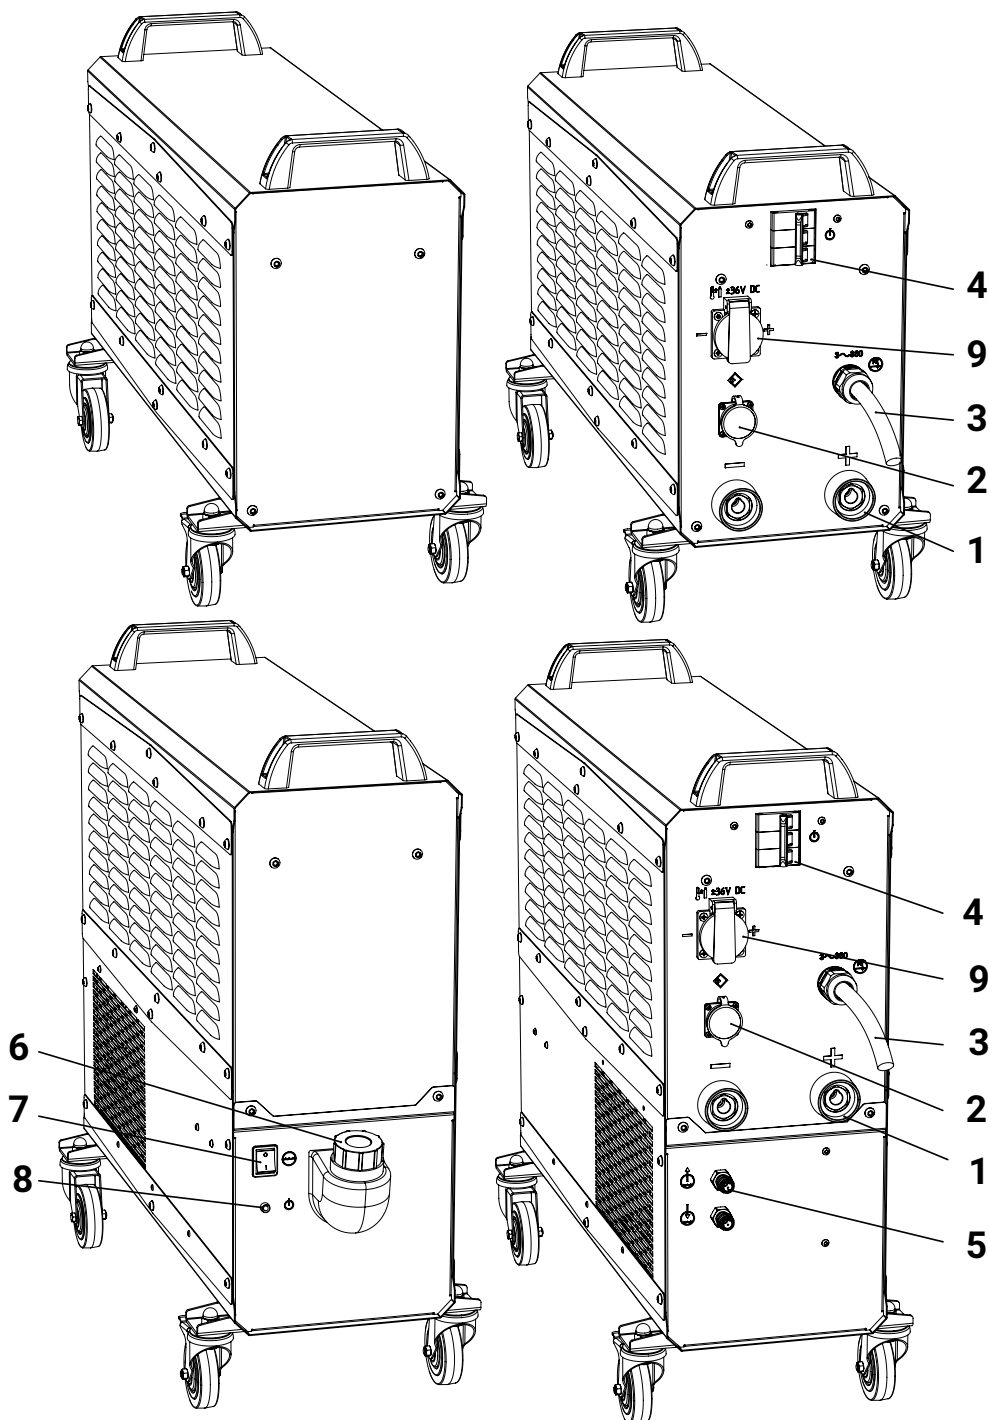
Расположение разъёмов на корпусе: 1 – байонетные сварочные разъёмы, 2 – разъём подключения УПП, 3 – сетевой кабель питания, 4 – выключатель аппарата, 5 – разъёмы подачи жидкости, 6 – горловина бака охлаждающей жидкости, 7 – выключатель жидкостного охлаждения, 8 – индикатор работы жидкостного охлаждения, 9 – разъём подключения подогревателя газа (опционально).
